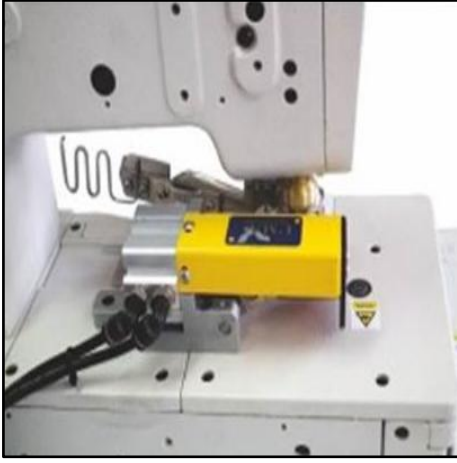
Arkalık ve Minder Kılıfı İçin Fitol Dikimi (Mevcut durum)
